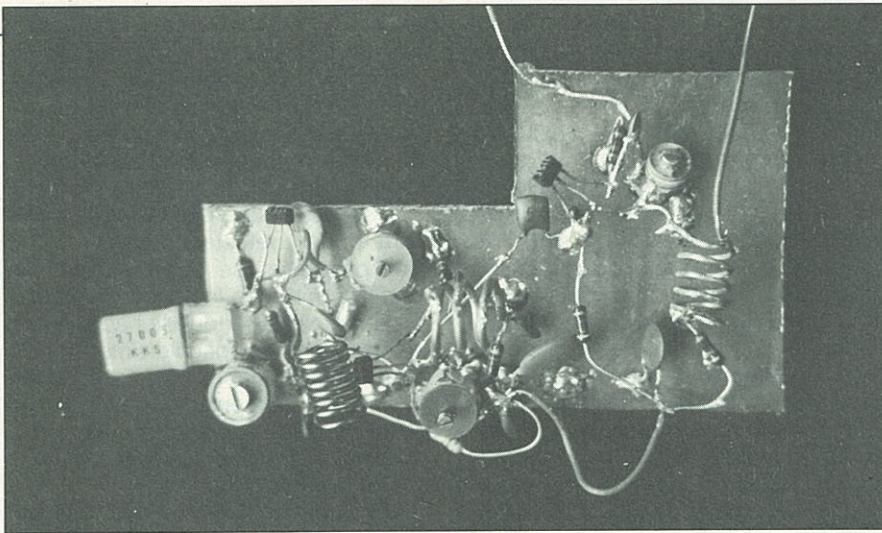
(B) Emisor de 144 MHz. El montaje no utiliza pistas. Los componentes se han soldado directamente entre sí, y sólo a la placa de cobre cuando van a masa. Las bobinas están perpendiculares. Esta técnica de montaje es muy adecuada para experimentar, por la facilidad de efectuar variaciones.
